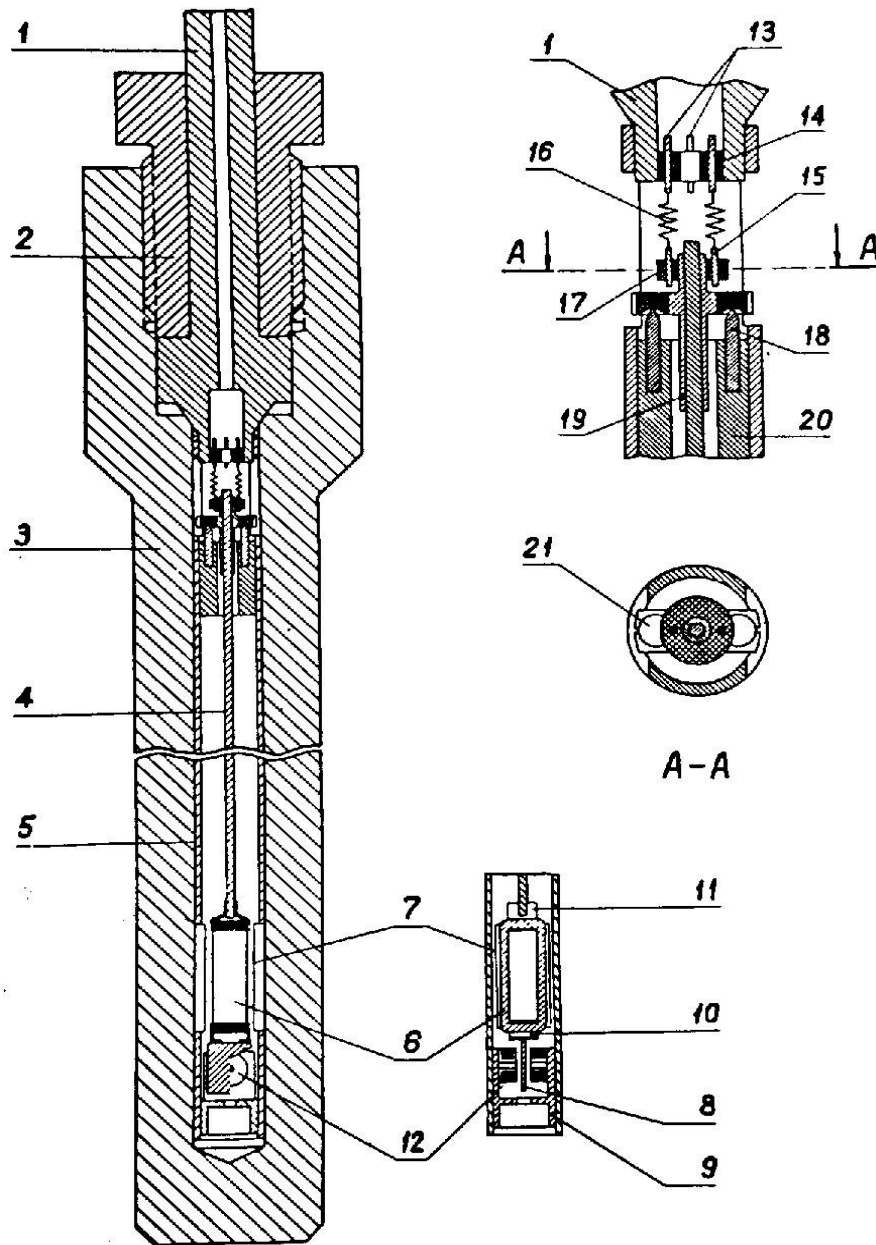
Маятникові ваги і камера високого тиску: 1 - головка; 2 – гвинт притискання; 3 - корпус камери; 4 - шток; 5 - корпус ваг; 6 - компенсаційна котушка; 7 - вікна; 8 - пелюстка датчика відхилення; 9 - обойма; 10,11 - перехідні скоби; 12 - котушки датчика відхилення; 13,15 - електричні перехідники; 14,17 - обойми; 16 - пружинні струмопідводи; 18 - голки; 19 - перехідник; 20 - опора; 21 – підп'ятники.
